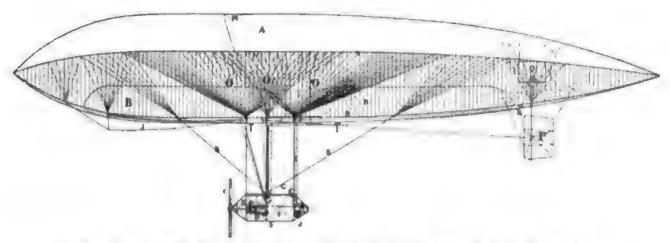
Zeichnung des Luftschiffes System "Astra-Torres". Schnitt durch die Gashülle. A = Ballon, B = Ballonetts, O = Innere Tragseile für die Gondel G, C = Propeller, D = Motor J = Ventilator, E = Kühler, P = Seitensteuer, Q = Stabilisierungsfläche, M = Ventil, I = Schleppseil.
